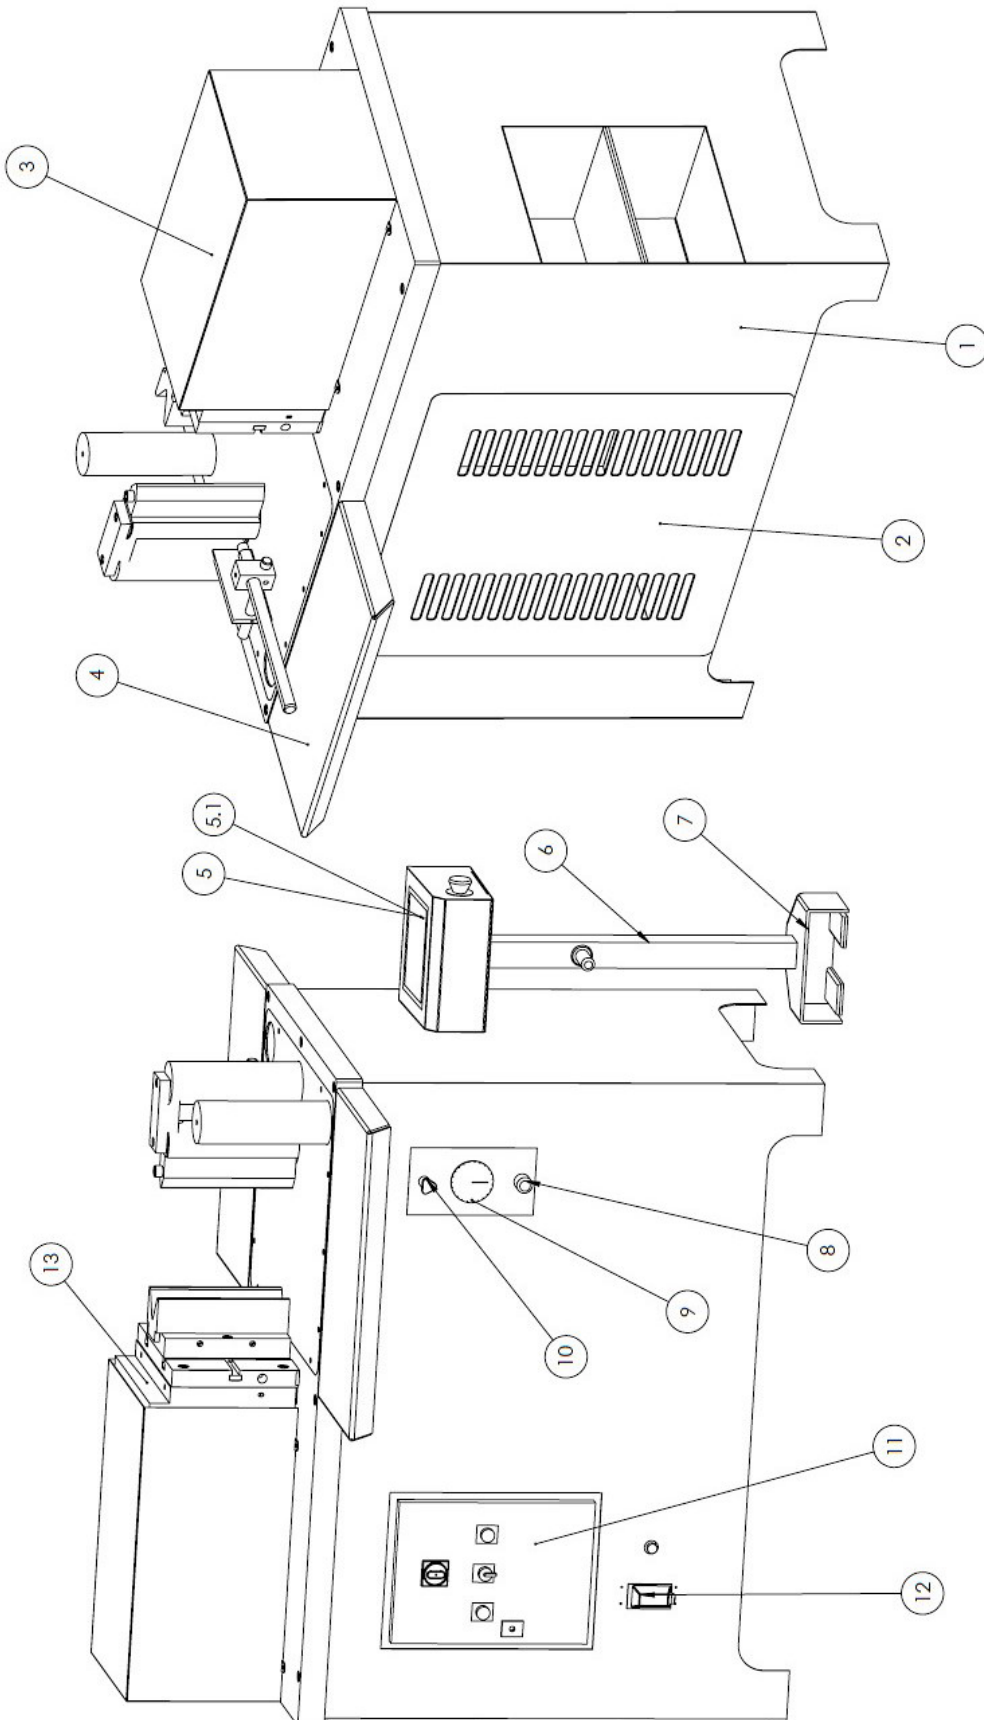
Ersatzteilzeichnung 1 Gesamtmaschine HBP 30
